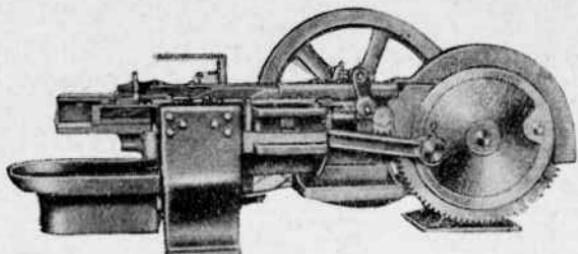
Устройство для подачи вручную длинных заготовок.
